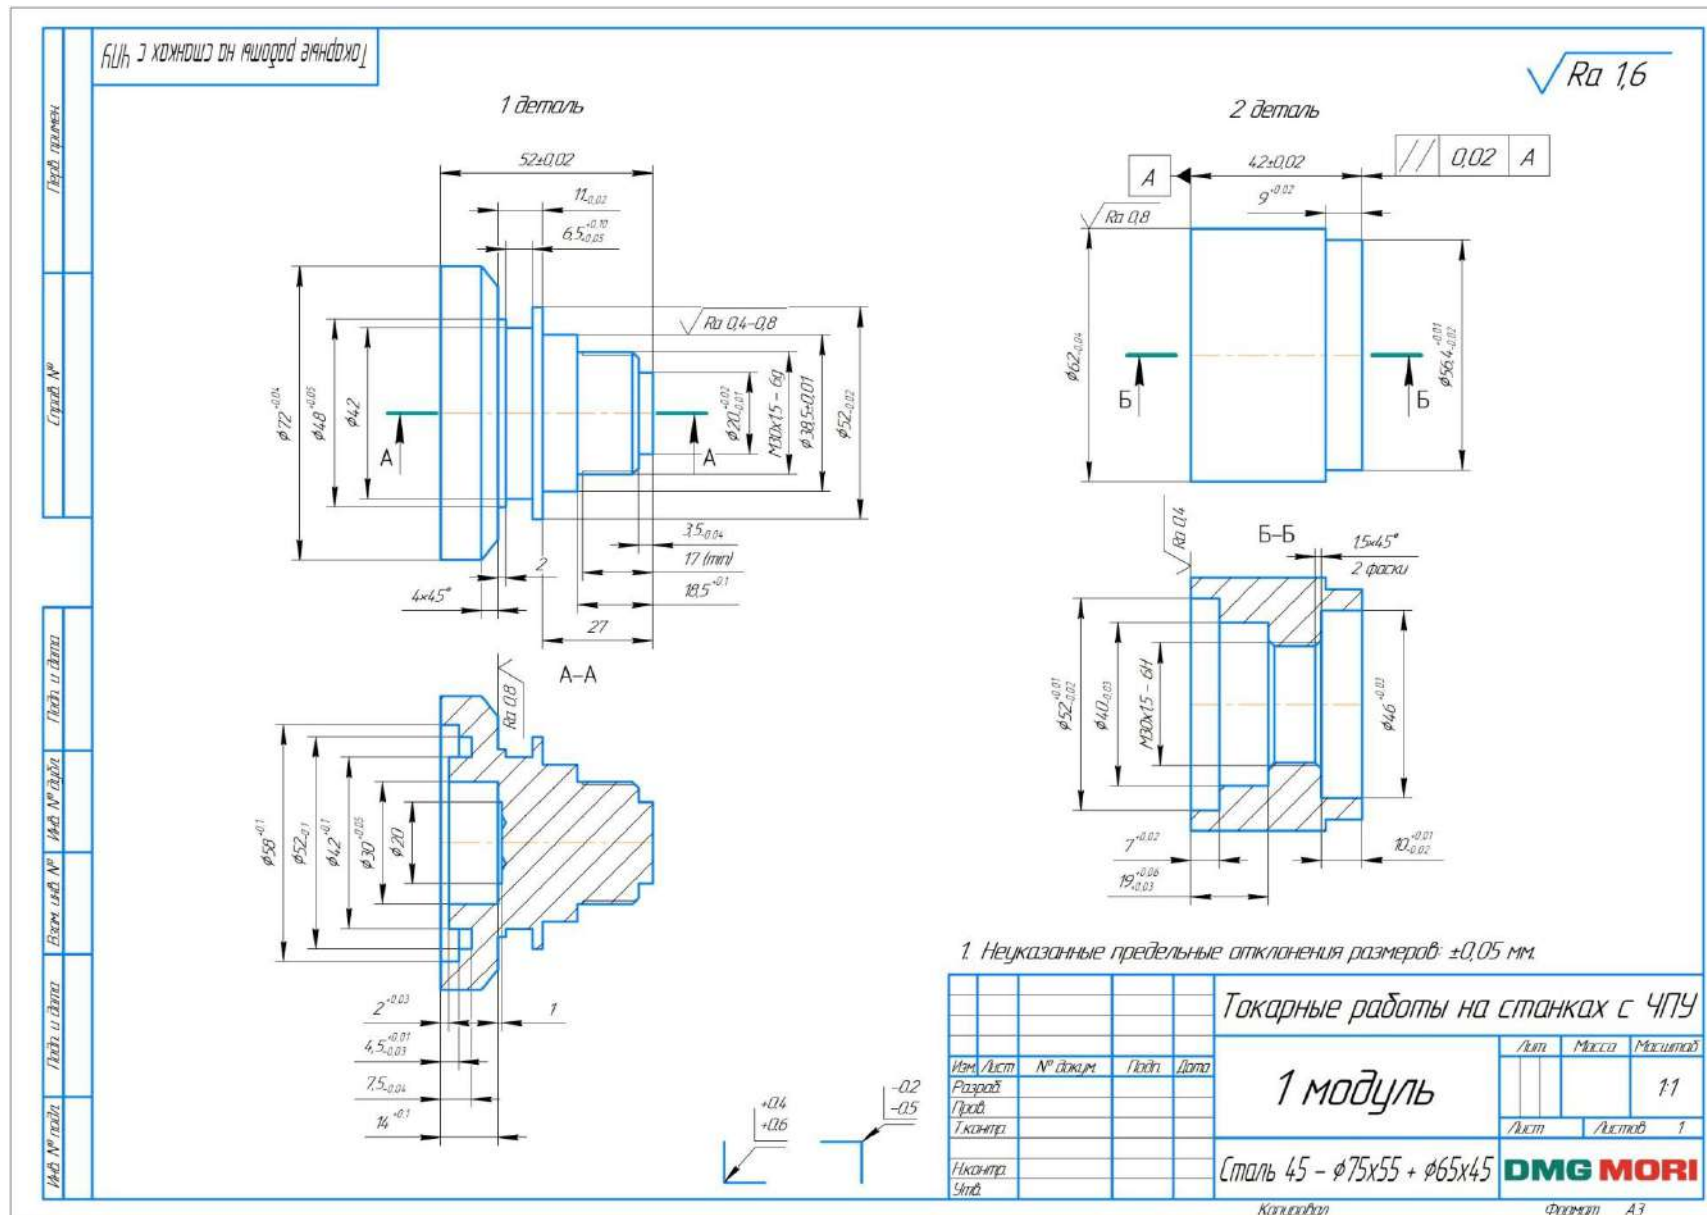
Модуль 1 Чертеж деталей Токарные работы на станках с ЧПУ
